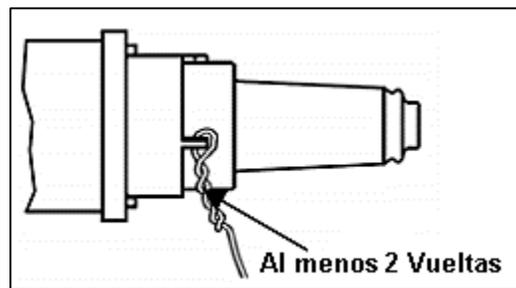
79. Paso 3 para la instalación del Bushing Insert [41]
